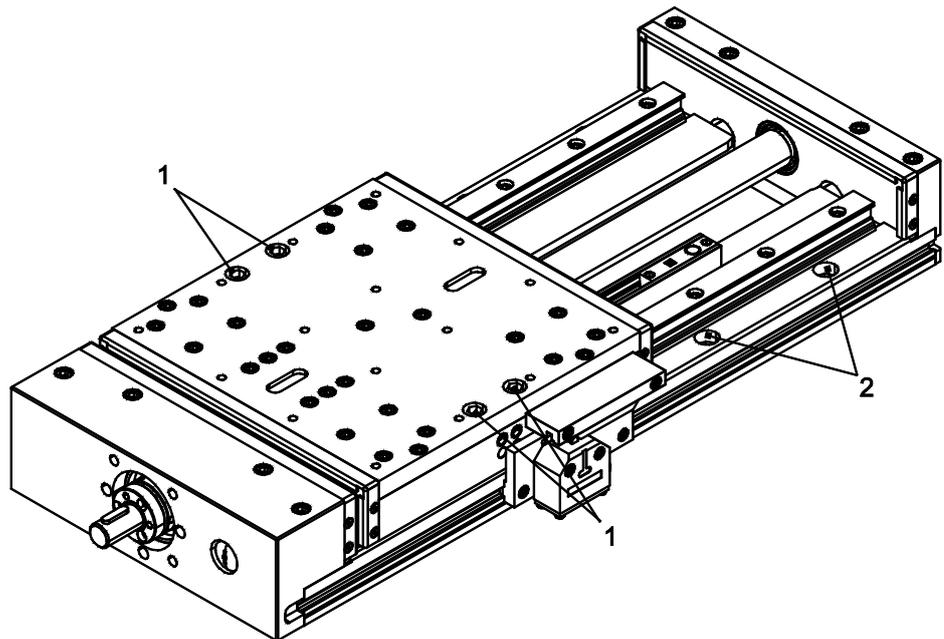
Montagebohrungen mit Gewindestift (1) und Befestigungsbohrungen (2)
